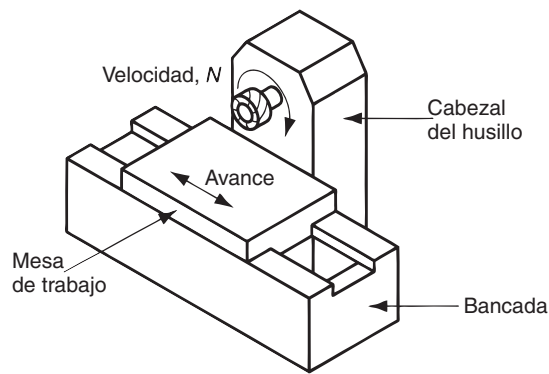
Máquina fresadora tipo cama simple de husillo horizontal.
